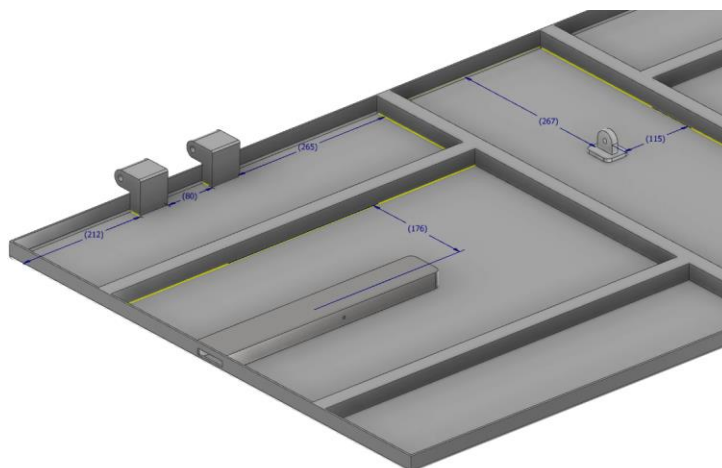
Soldadura da guia da fechadura, dos segmentos da dobradiça e do fixador do amortecedor da porta de segurança.
